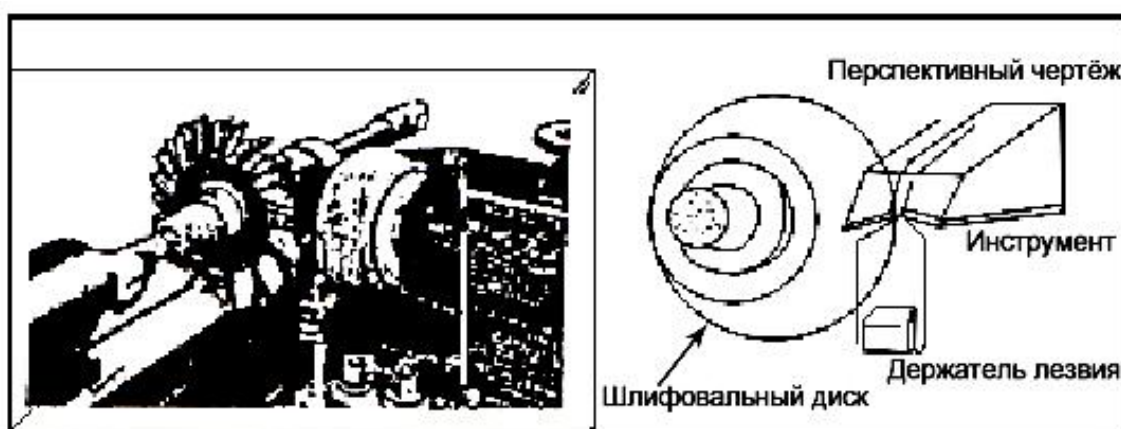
Схема взаимосвязи инструмента, шлифовального диска и держателя лезвия
